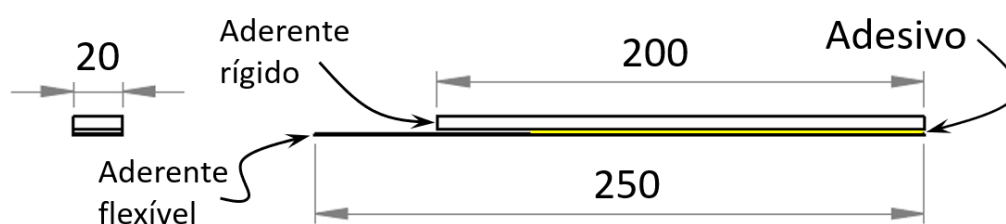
Geometria do conjunto provete rígido e flexível (dimensões em mm).
